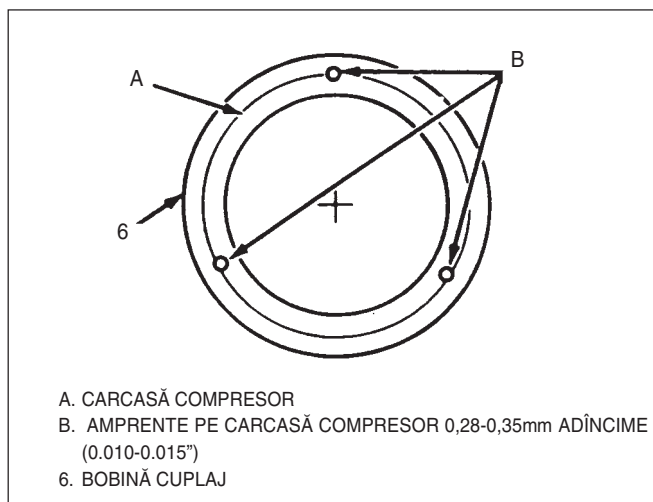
Detaliu cap amprentat pt fixare bobină cuplaj
